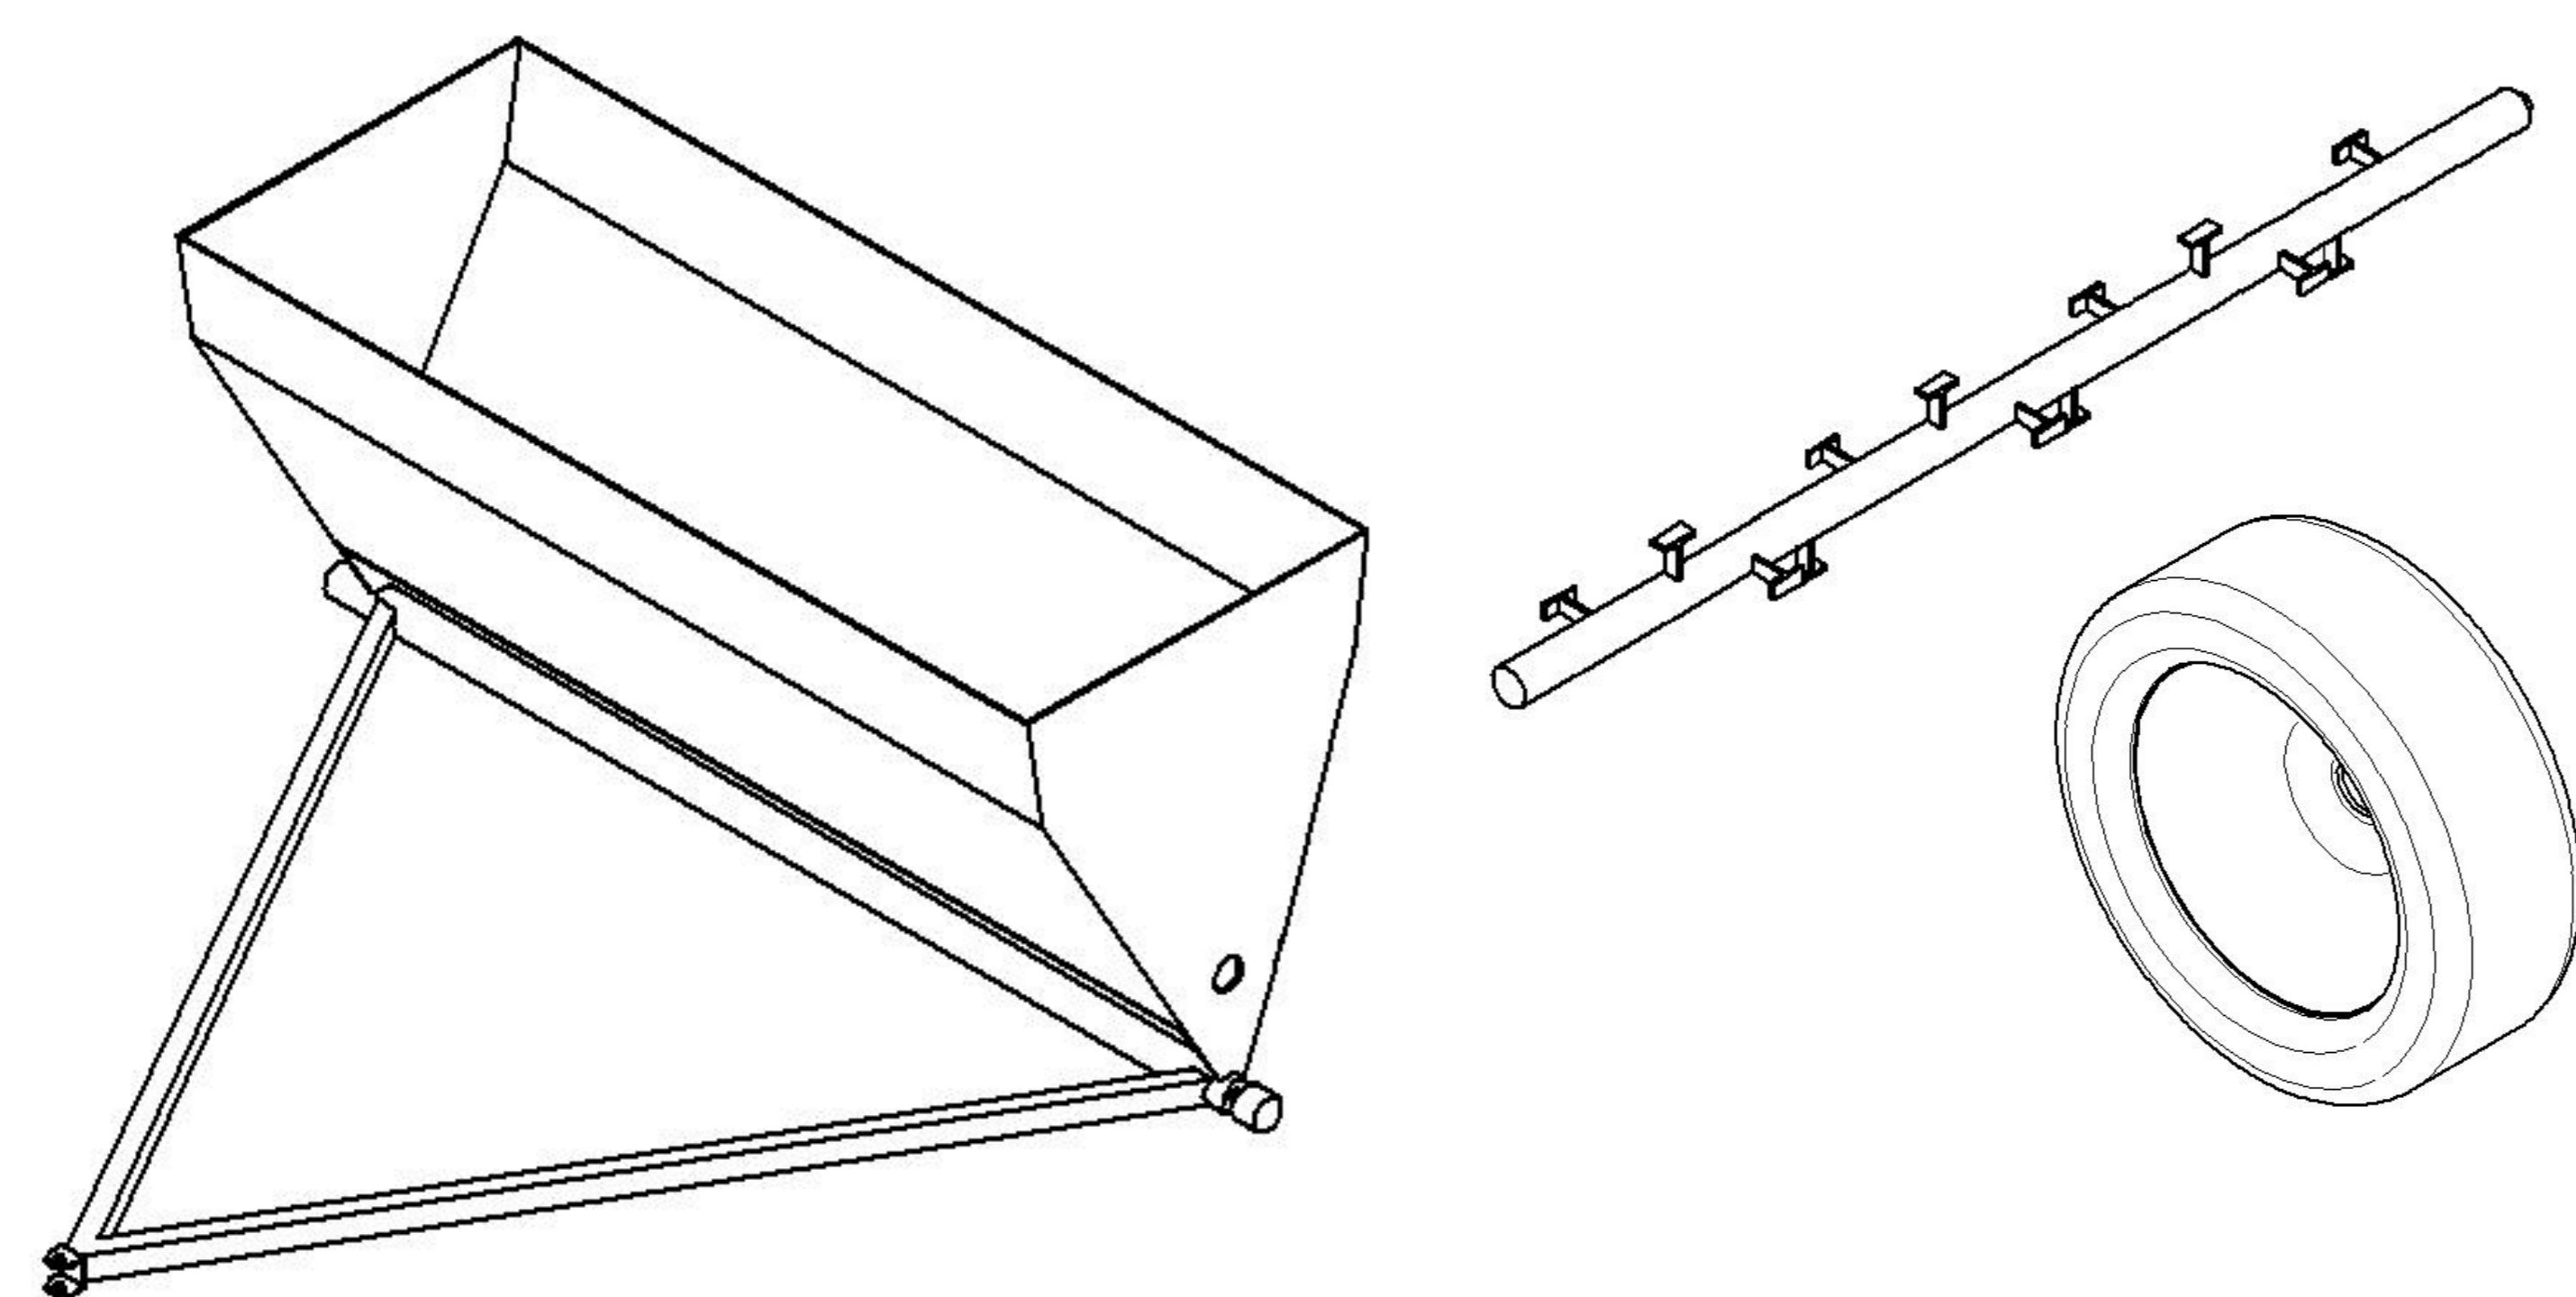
Componentes básicos da calcareadora (reservatório com chassi, rotor e roda).
